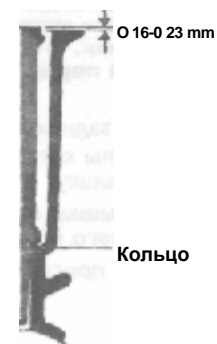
Взаиморасположение гильзы цилиндра, кольца и блока цилиндров — Двигатель B280F
